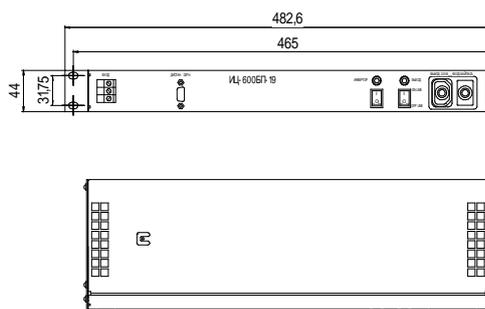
Габаритный чертеж ИЦ-600 БП-19
